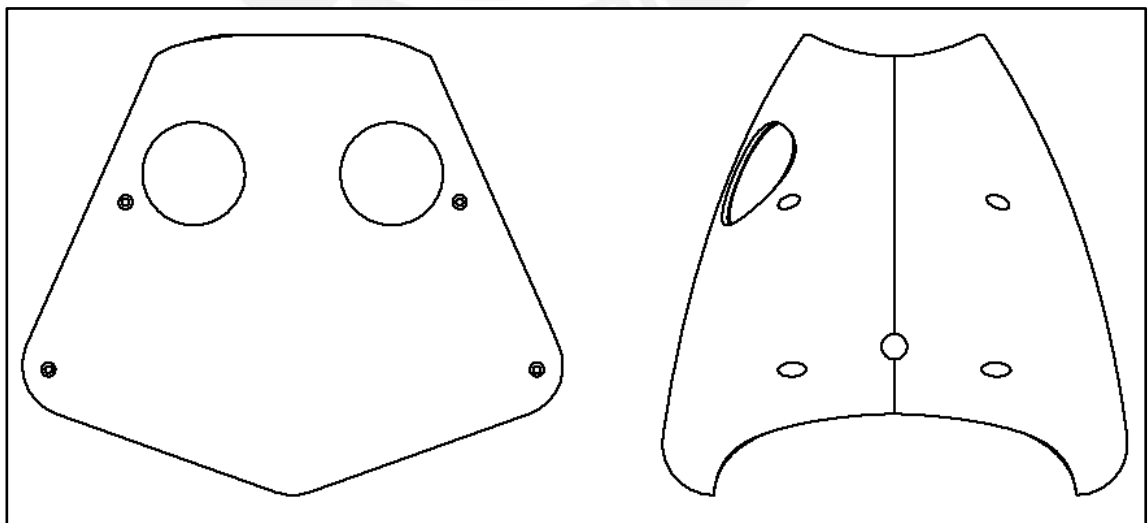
Vista frontal y lateral de la carcasa que forma el torso de MUQUI
